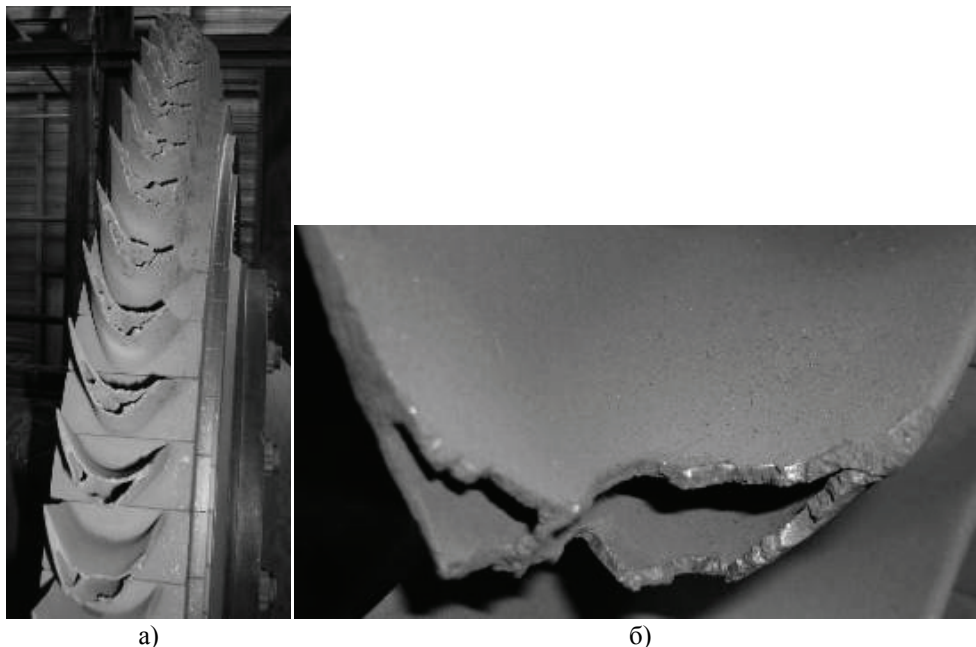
Вид перовой части лопаток ТВД после аварии: а – общий вид в сборке; б – вид поверхности излома пера исследуемой лопатки
